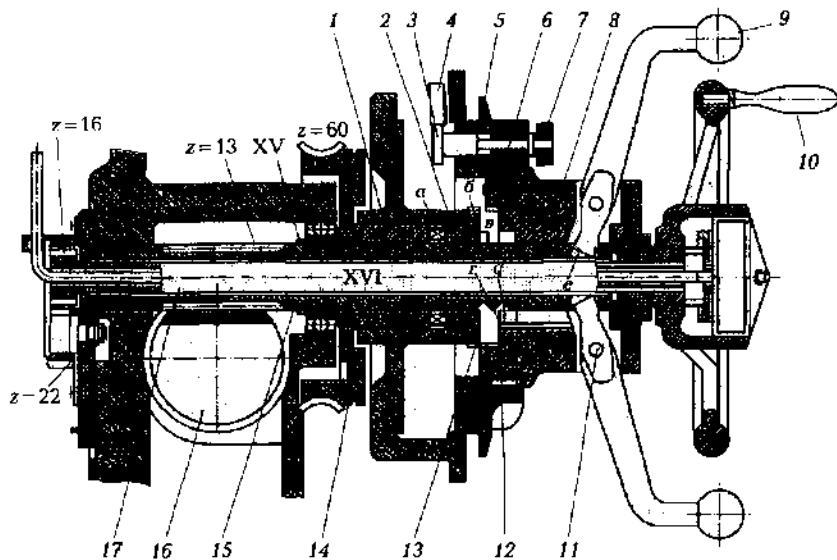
Механизм перемещения шпинделя и шпиндельной бабки по траверсе:
